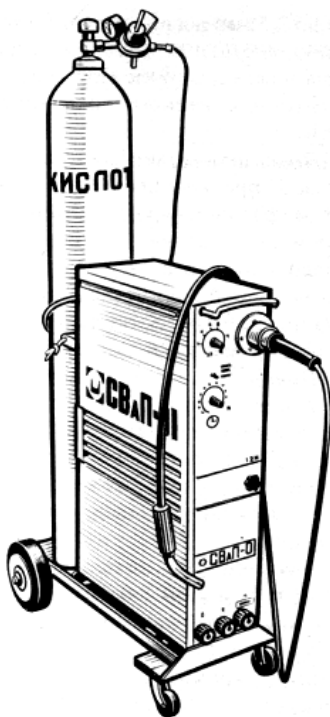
Сварочный полуавтомат СВАП-1
